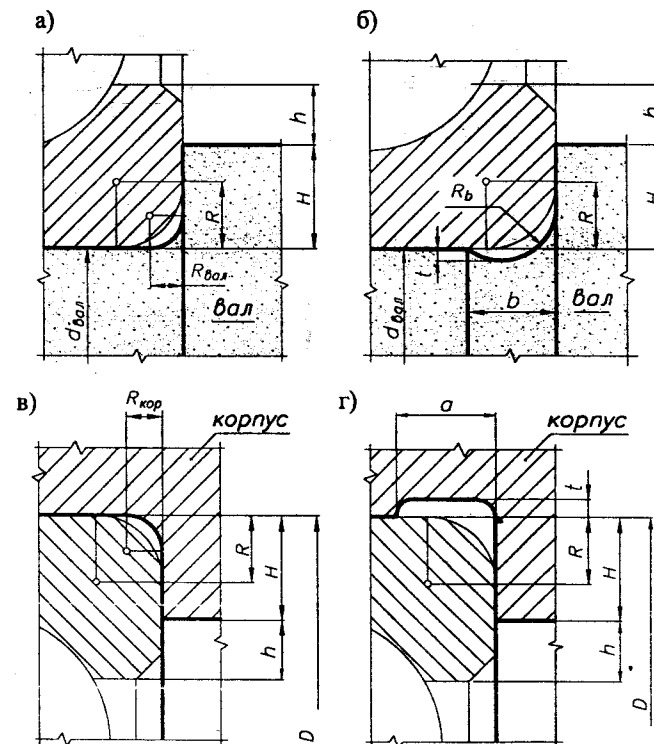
Радиусы закруглений и размеры подточек: а), б) для вала; в), г) для корпуса
